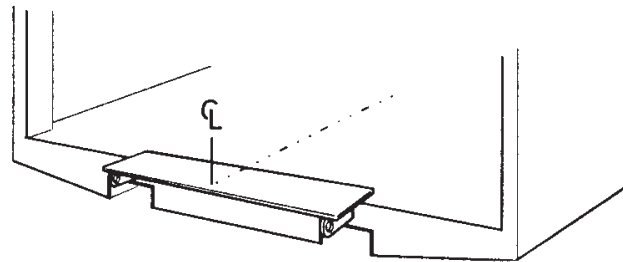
Die Montagevorrichtung an der Hecktraverse anschrauben oder anschweißen Artikelnr. 51724TL für Z 1500/2000
